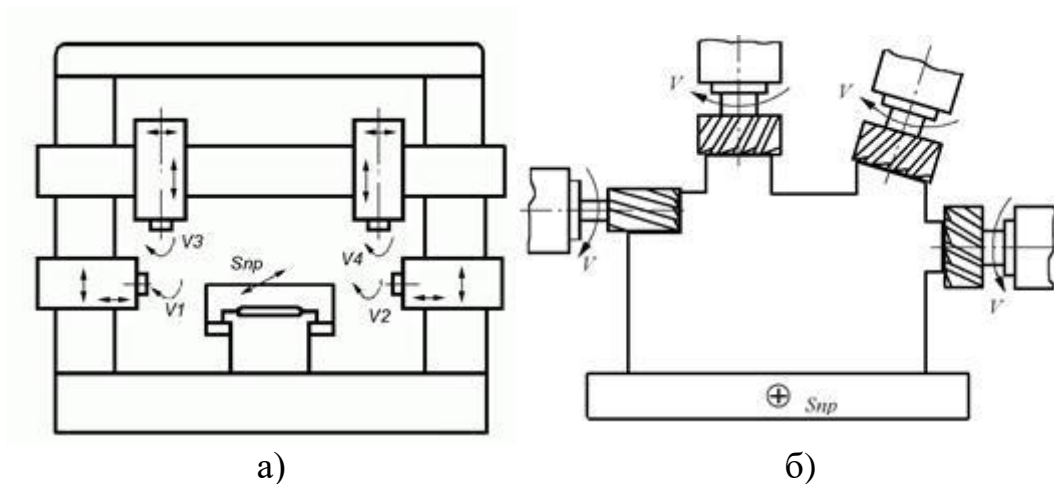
Схемы компоновки продольно - фрезерного станка (а) и обработки поверхностей на продольно - фрезерном станке (б)
